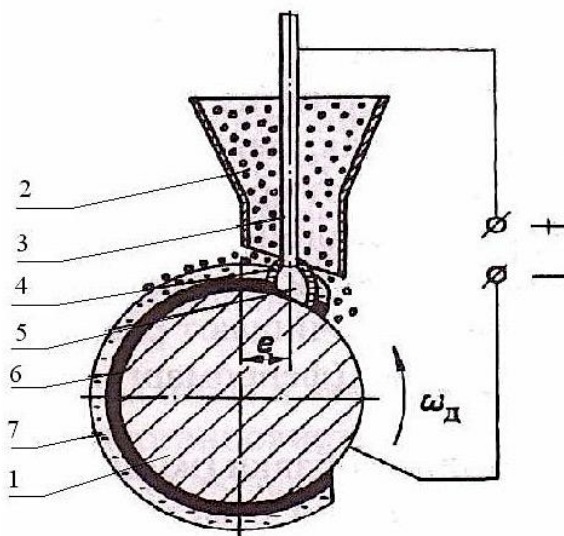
Наплавка цилиндрической детали под слоем флюса:
